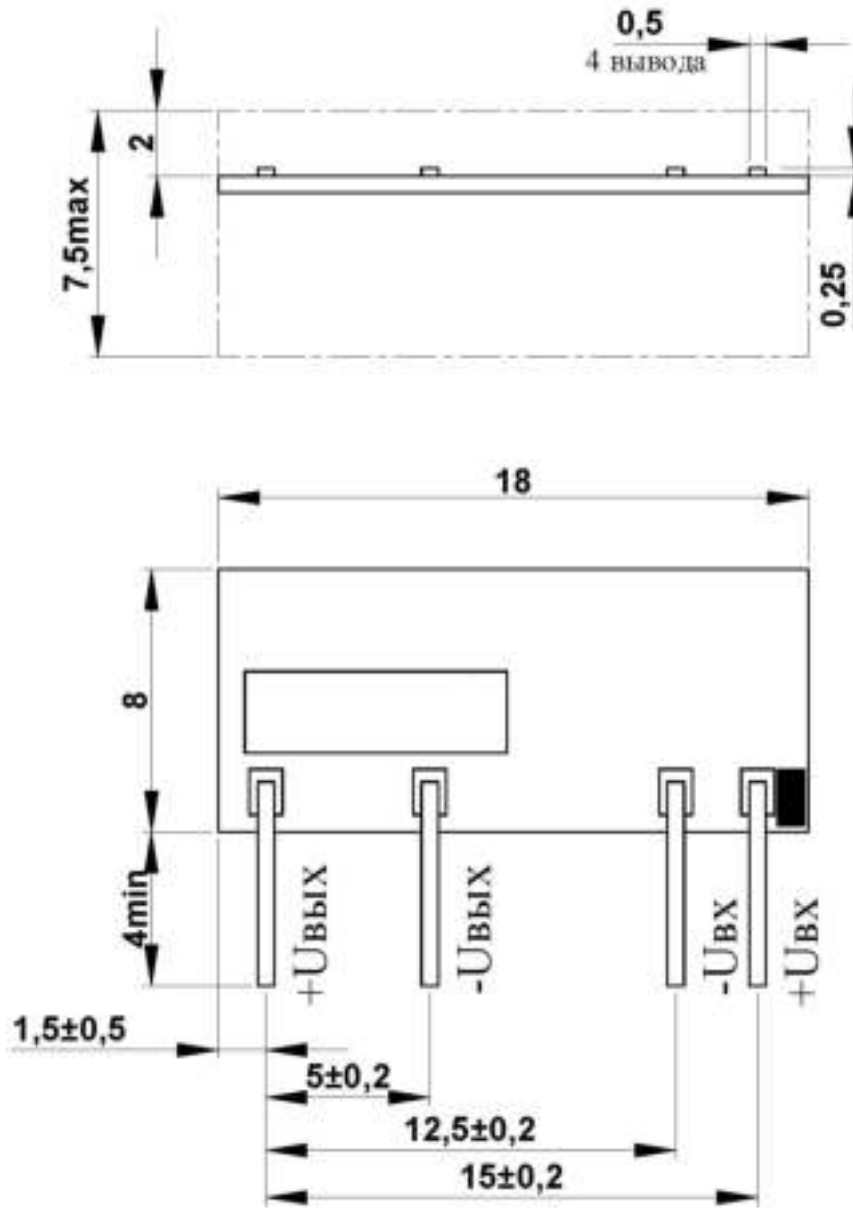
Габаритный чертеж модулей в конструктивном исполнении «В»
